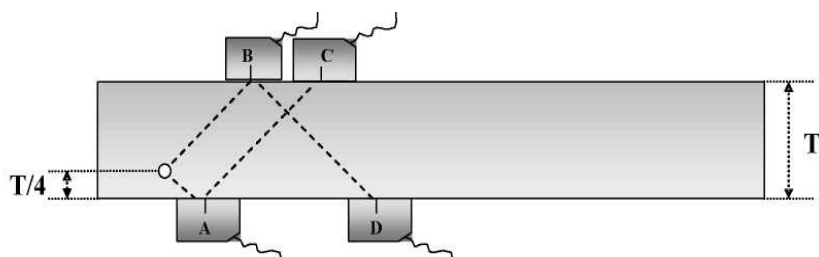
Схема побудови DAC – кривої на КЗ без фарбового покриття
